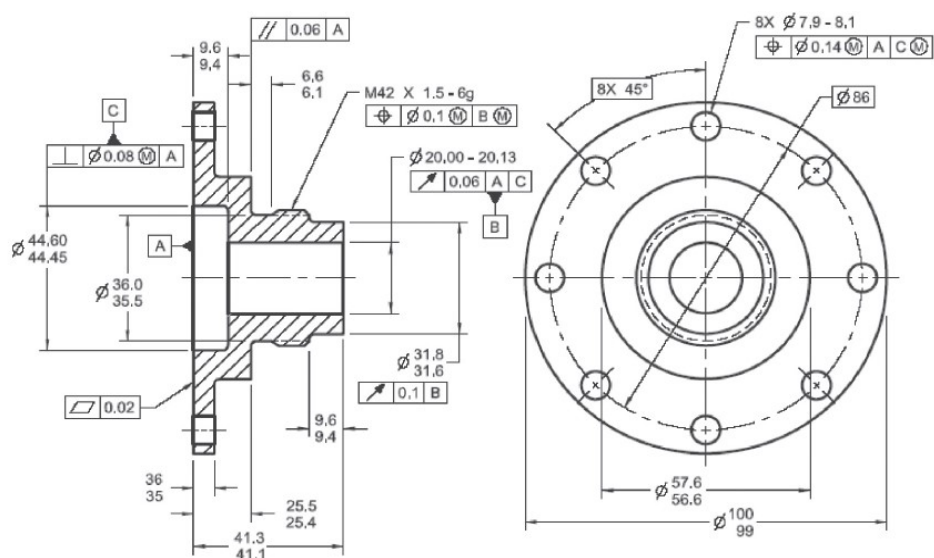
Exemplo de desenho técnico com linguagem GD&T.
